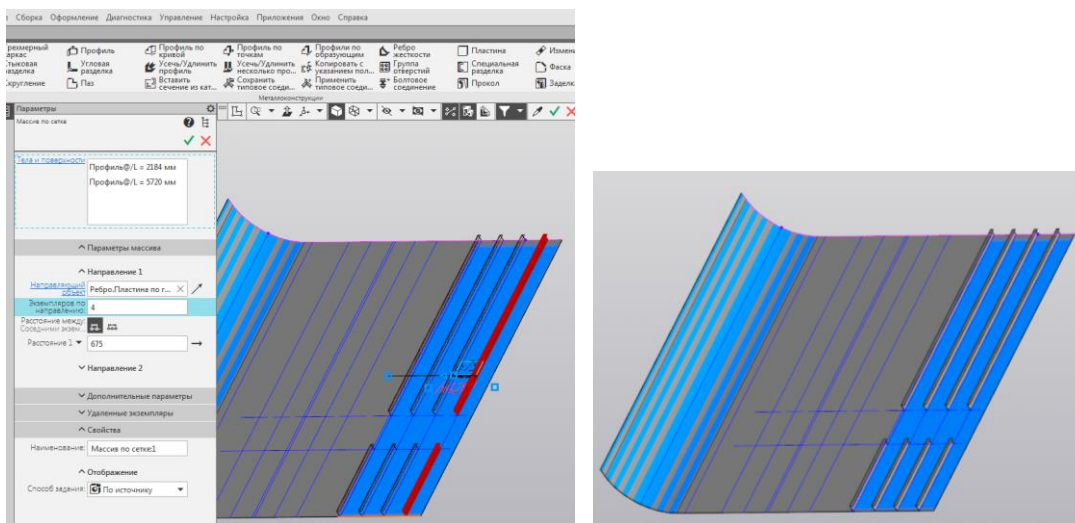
Расстановка нескольких одинаковых балок по поверхности обшивки:
